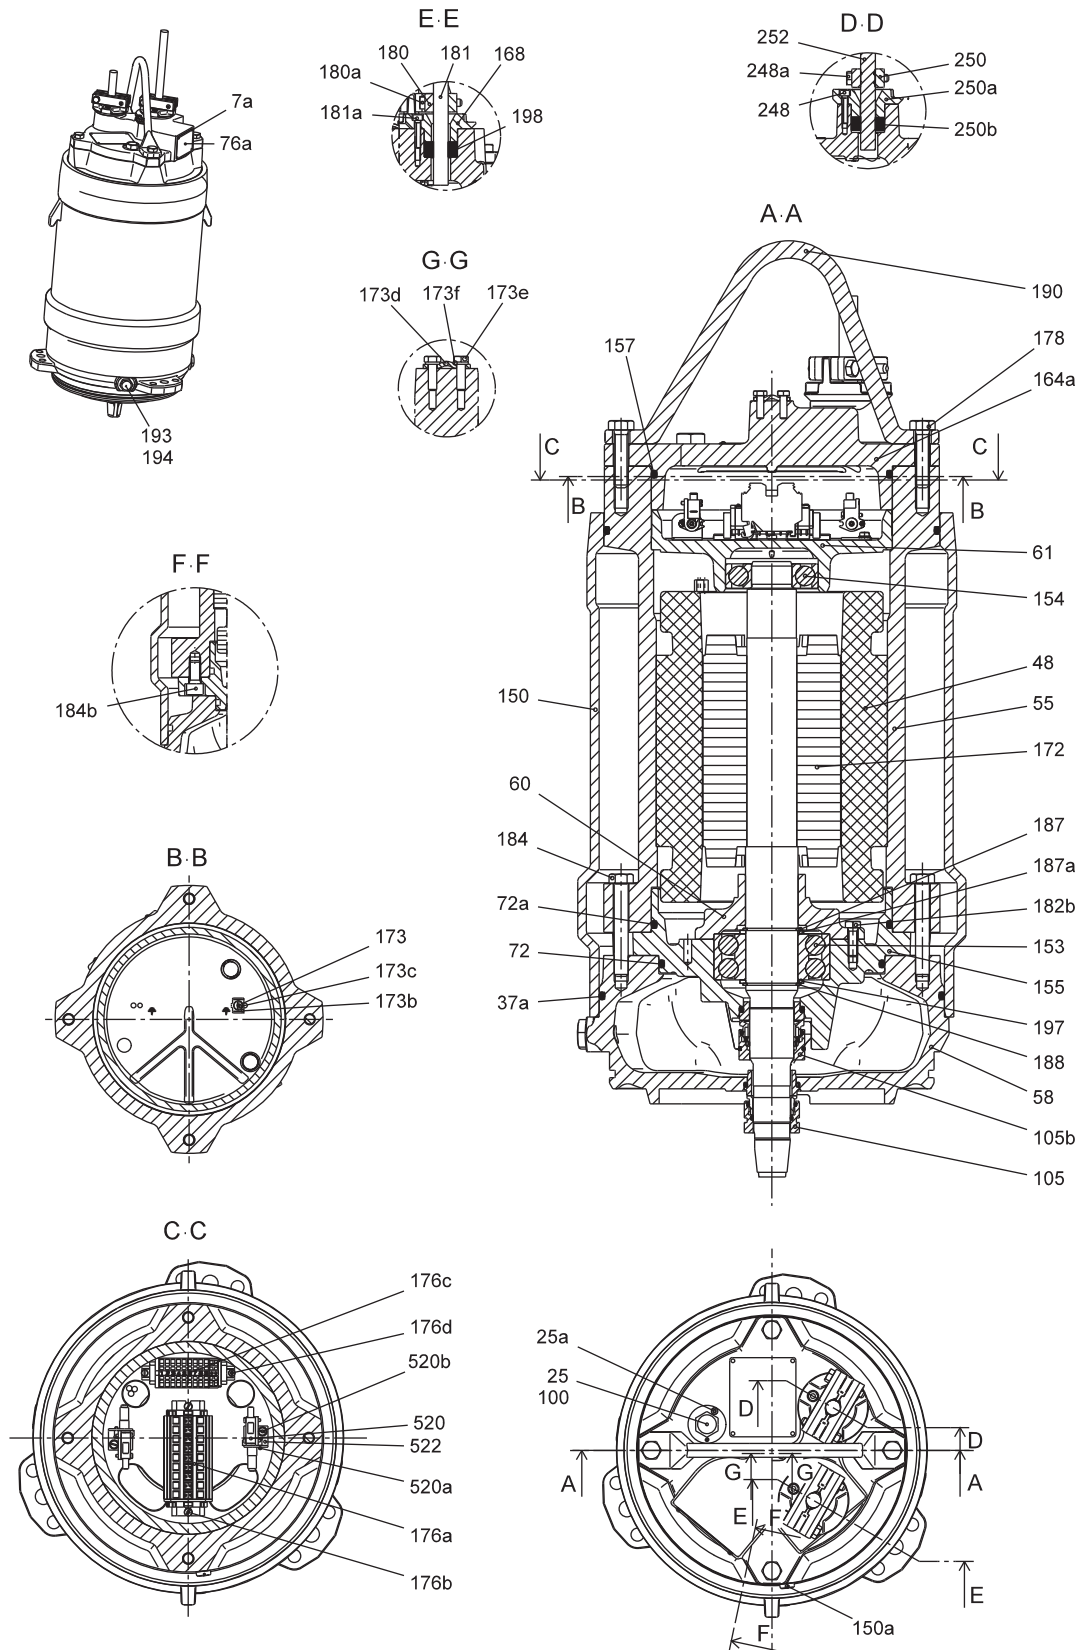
Взрывозащищённый двигатель без охлаждающего кожуха
